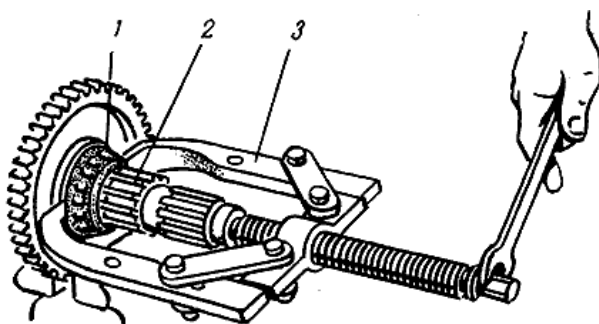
Спрессовка внутренней обоймы подшипника со вторичного вала: 1 — внутренняя обойма; 2 — вторичный вал; 3 — съемник
